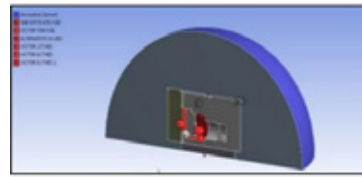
Sac Malzeme Özelliklerinin Modele Tanıtılması
